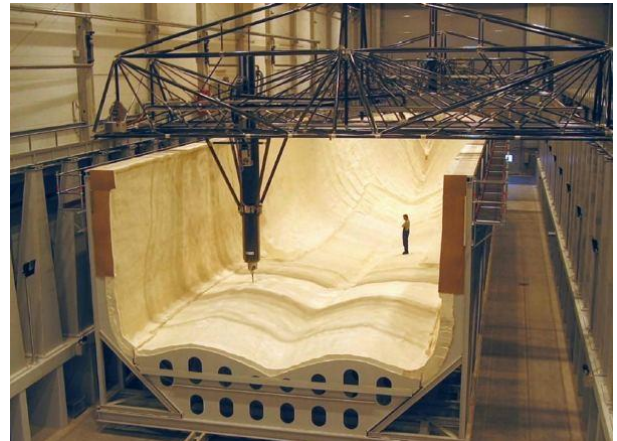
EEW ProTec overhead CNC machine. Gemakkelijk om te bouwen naar een 3D printer.
